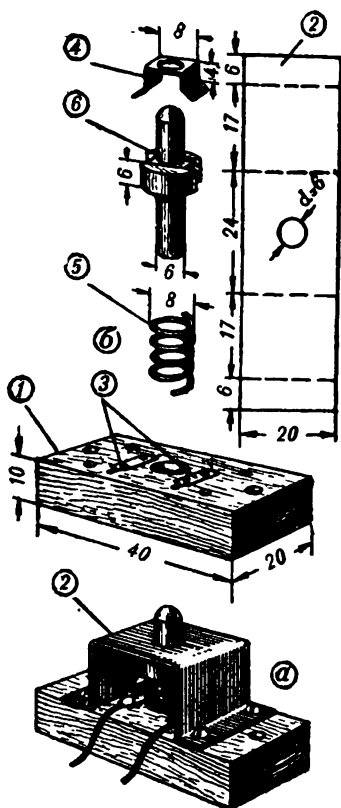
Конструкция самодельной кнопки: а — внешний вид; б — конструкция деталей кнопки.
